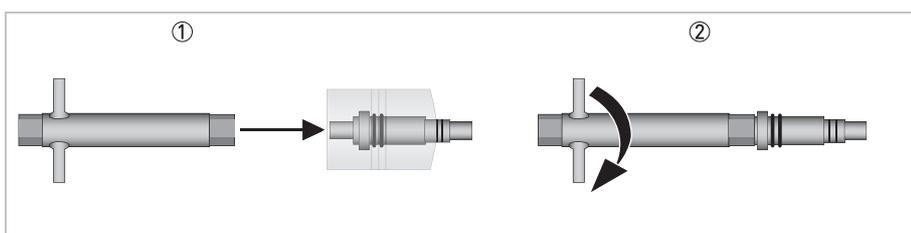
Установка измерительного преобразователя в инструмент
